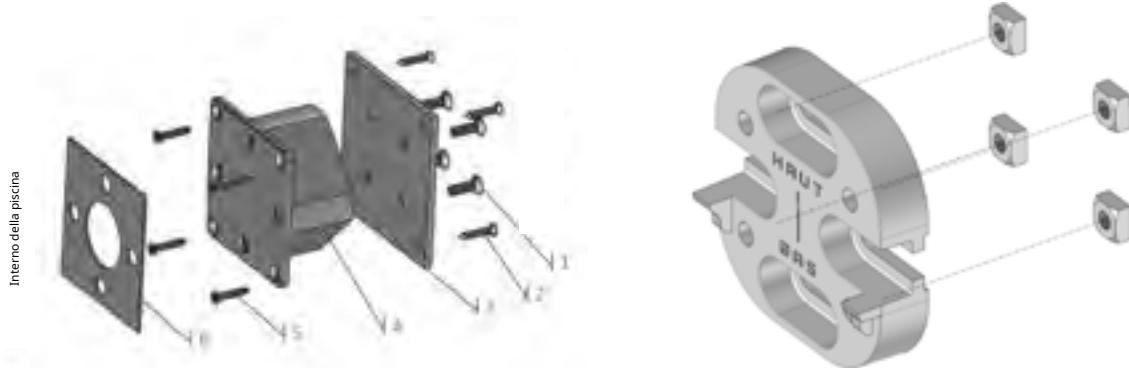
Montaggio dell'unità di montaggio cuscinetti
